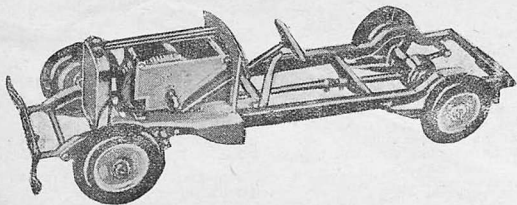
Собранный из деталей автоконструктора шасси автомобиля
